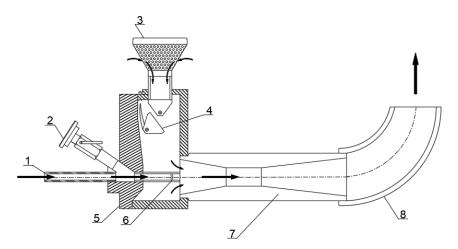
Устройство для смешивания биогаза с воздухом: 1 — входной патрубок; 2 — штуцер для манометра; 3 — воздушный сетчатый фильтр; 4 — обратный клапан; 5 — крышка; 6 — сопло; 7 — диффузор; 8 — выходной патрубок
